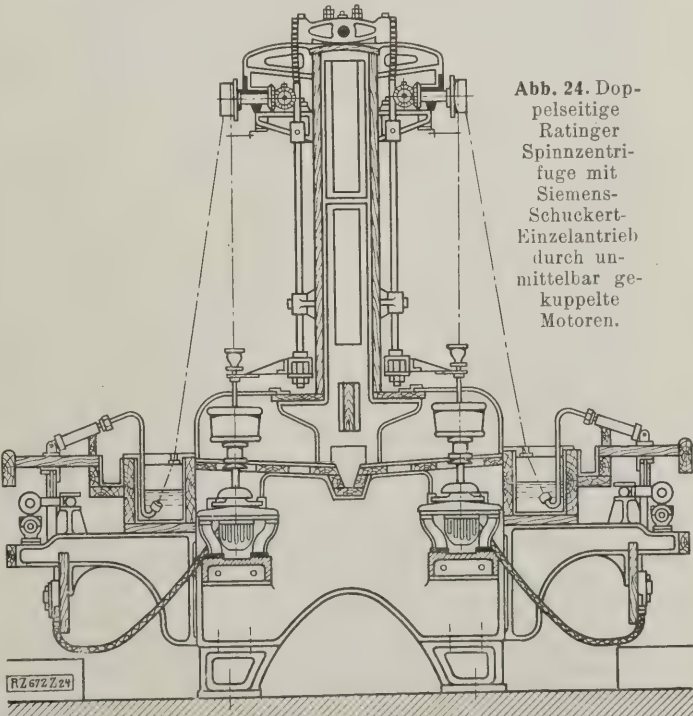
Doppelseitige Rätiger Spinnzentrifuge mit Siemens-Schuckert-Einzelantrieb durch unmittelbar gekuppelte Motoren.
